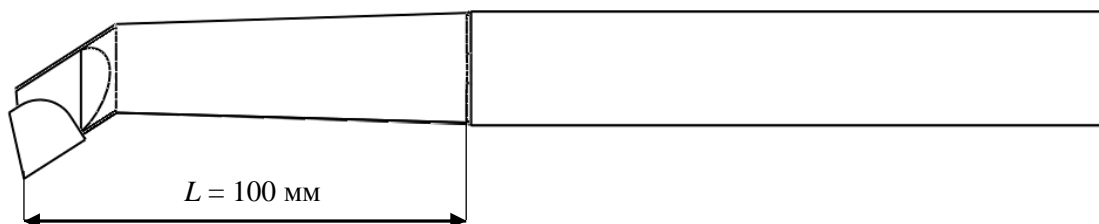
Сборная твердотельная модель стандартного расточного резца с твердосплавной пластиной по [1]
